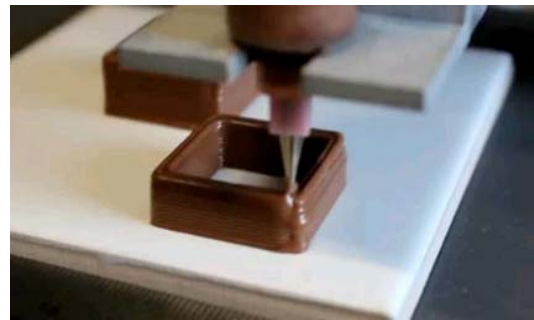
2. Impresión 3D de chocolate. Fuente: www.impresoras3d.com [1]
